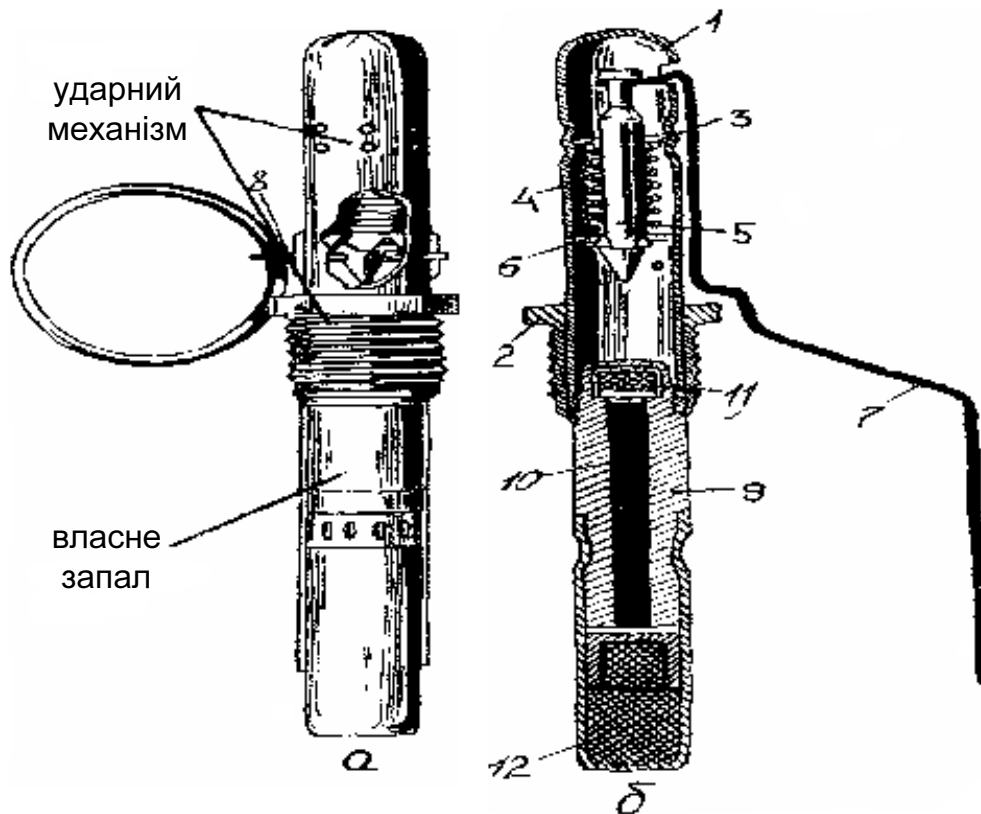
Запал гранати УЗРГМ: а - загальний вигляд; б - у розрізі; 1 - трубка ударного механізму; 2 - з'єднувальна втулка; 3 - спрямовуюча шайба; 4 - бойова пружина; 5 - ударник; 6 - шайба ударника; 7 - спусковий важіль; 8 - запобіжна чека; 9 - втулка сповільнювача; 10 - сповільнювач; 11 - капсуль-запалювач; 12 - капсуль-детонатор
